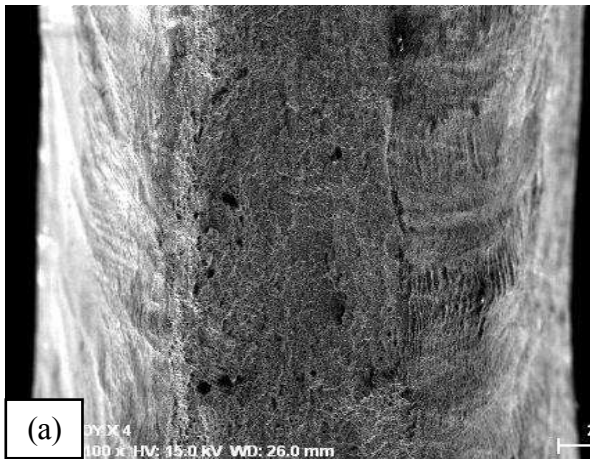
Análisis de la fractura mediante MEB en las probetas sometidas a tensión de la unión soldada tipo C.
